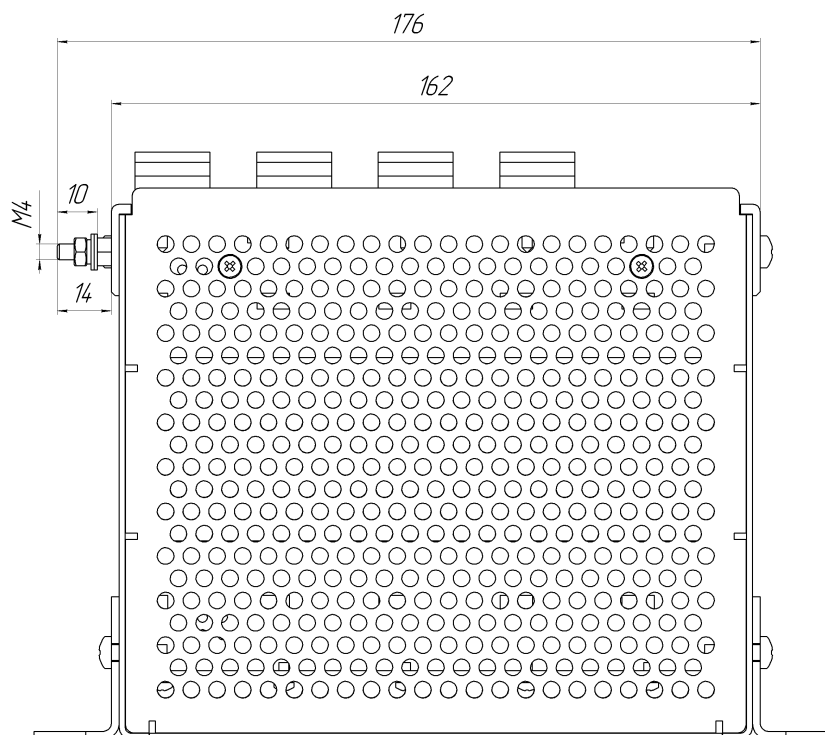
Установочные размеры ARIS-2305, мм (вид сверху)
